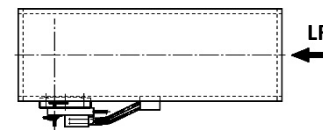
ripresa, esecuzione sinistra, vista dall'alto
